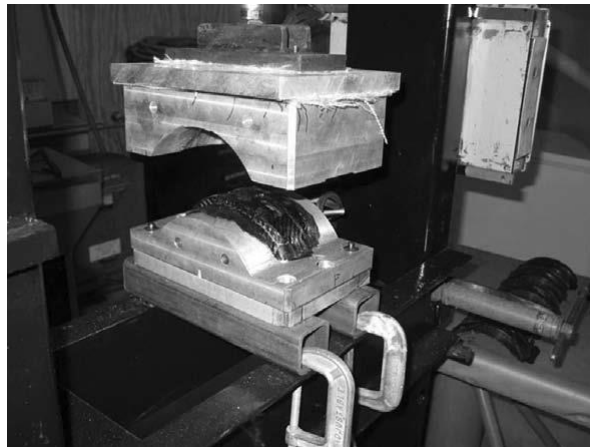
Moldeo por compresión de preimpregnado de fibra de carbono [10].
